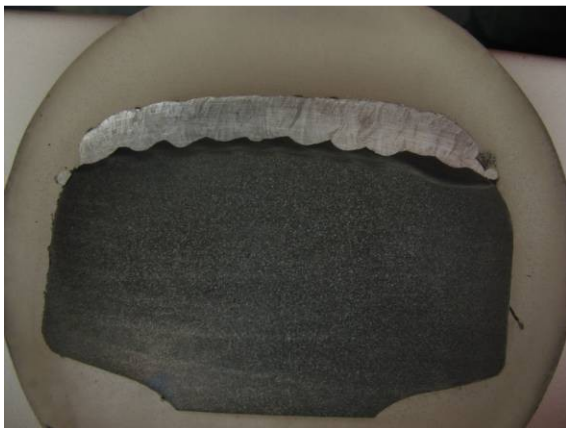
Makroštruktúra návaru vzorky A3 pri predhreve 350°C
